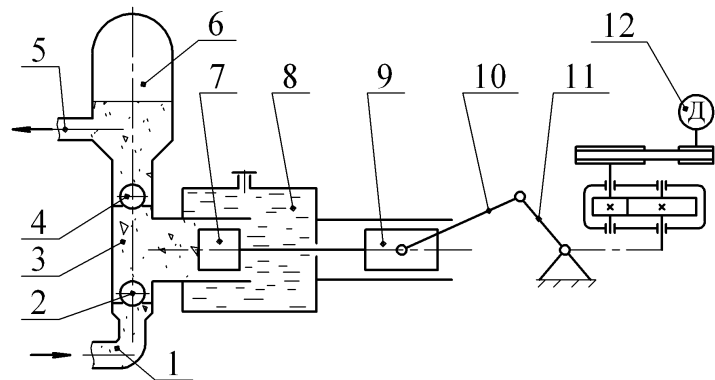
Конструктивна схема однопоршневого бездіафрагмового розчинонасоса одинарної дії: 1 – всмоктувальний патрубок; 2 – всмоктувальний клапан; 3 – робоча камера; 4 – нагнітальний клапан; 5 – нагнітальний патрубок; 6 – компенсаційний ковпак; 7 – робочий поршень; 8 – проміжна рідина; 9 – допоміжний поршень; 10 – шатун; 11 – кривошип; 12 – двигун із приводом.
